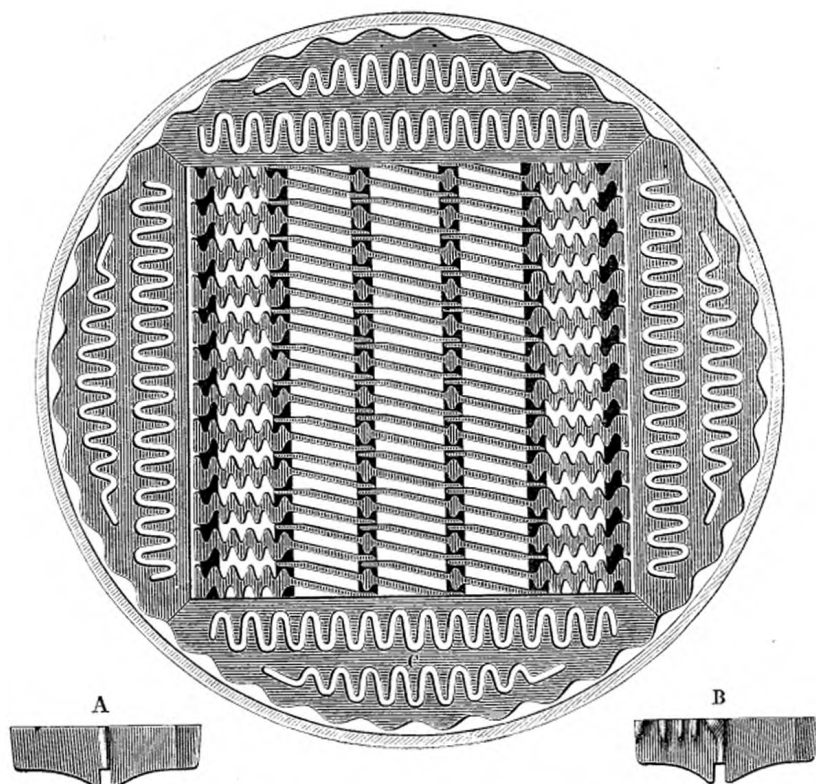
PLAN DE GRILLE SECTIONNELLE RONDE.
